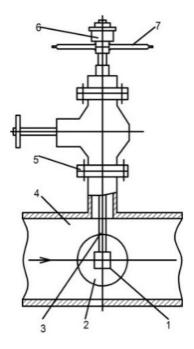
Индукционный расходомер ИР-5Р: I – преобразователь; 2 – водяной поток; 3 – штанга; 4 – рабочий трубопровод; 5 – фланец; 6 – клеммная коробка; 7 – рукоятка
